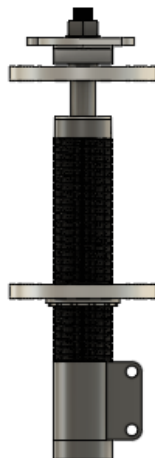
Conjunto amortiguador con piezas de montaje.
